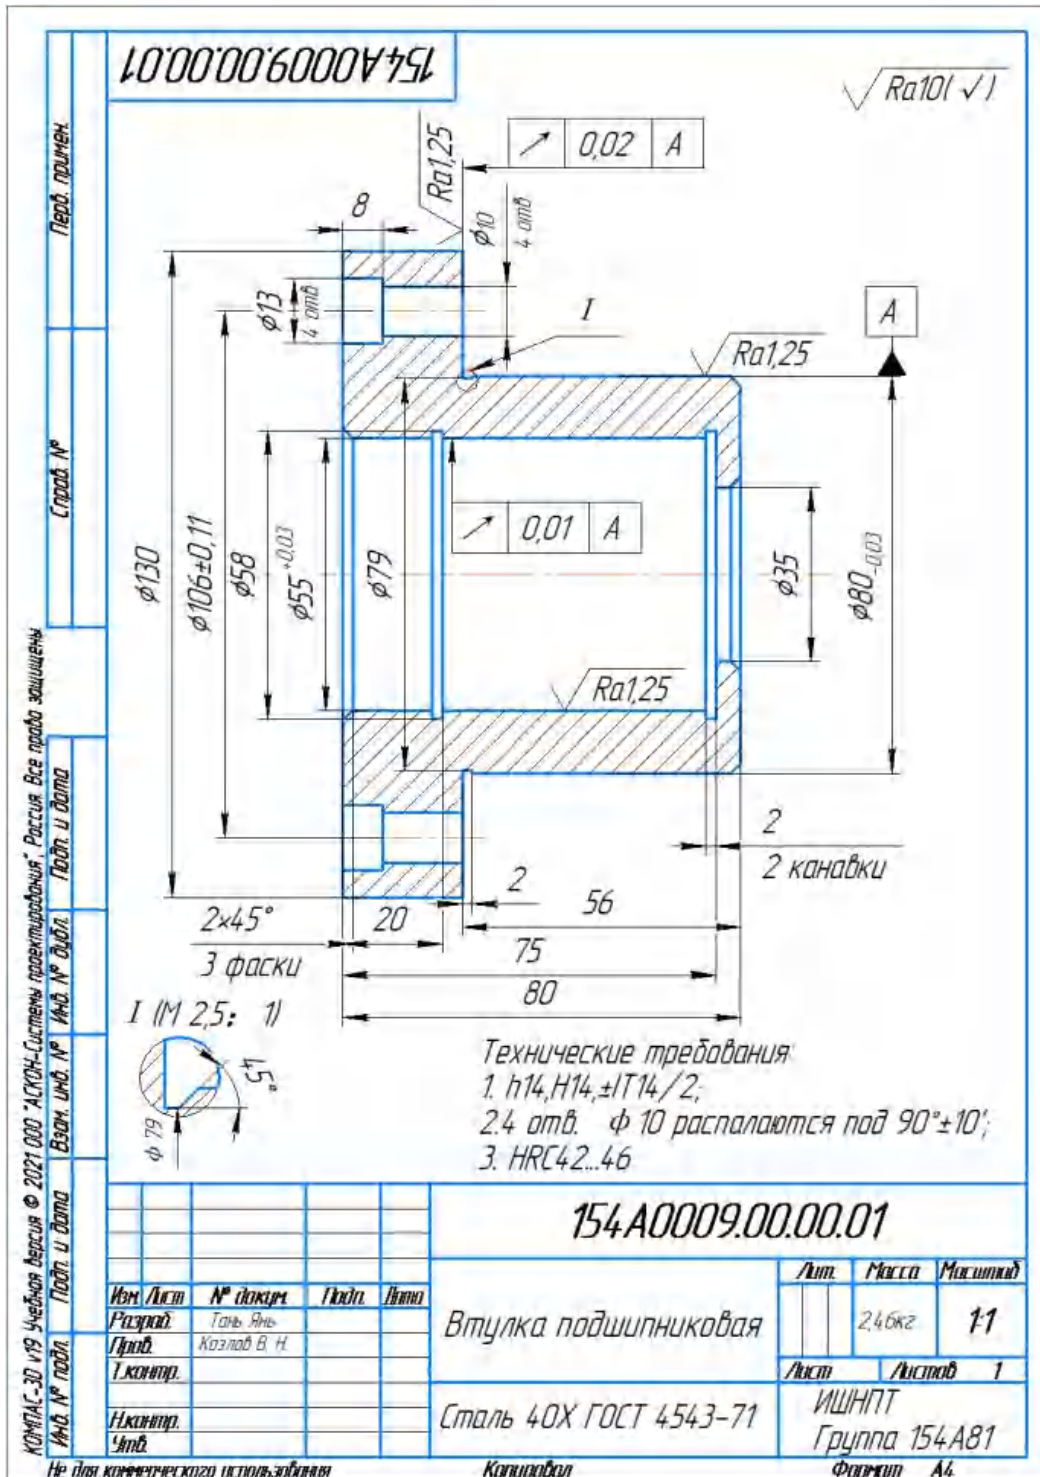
Эскиз детали «Втулка подшипниковая»
